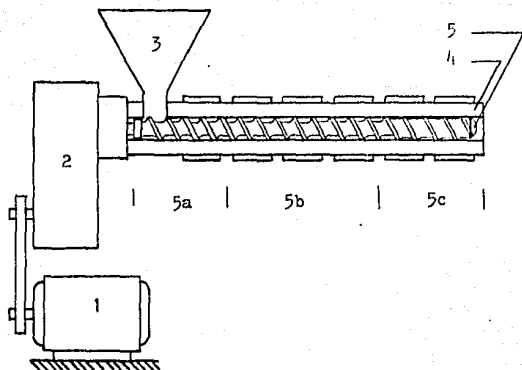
Diagrama de un extrusor con sus principales componentes: 1) Motor; 2) Reductor de engranes; 3) Tolva; 4) Cilindro de calentamiento; 5) Tornillo sin fin con 3 secciones: 5a) Alimentación; 5b) Fundición-Transición; 5c) Medición.
